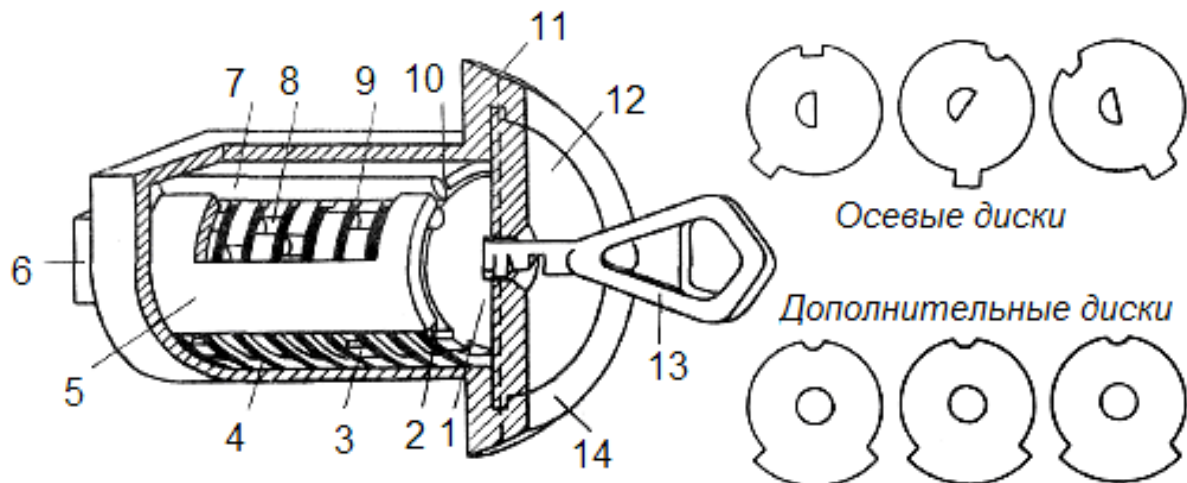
Устройство цилиндрического механизма замка типа «Аблой»:
